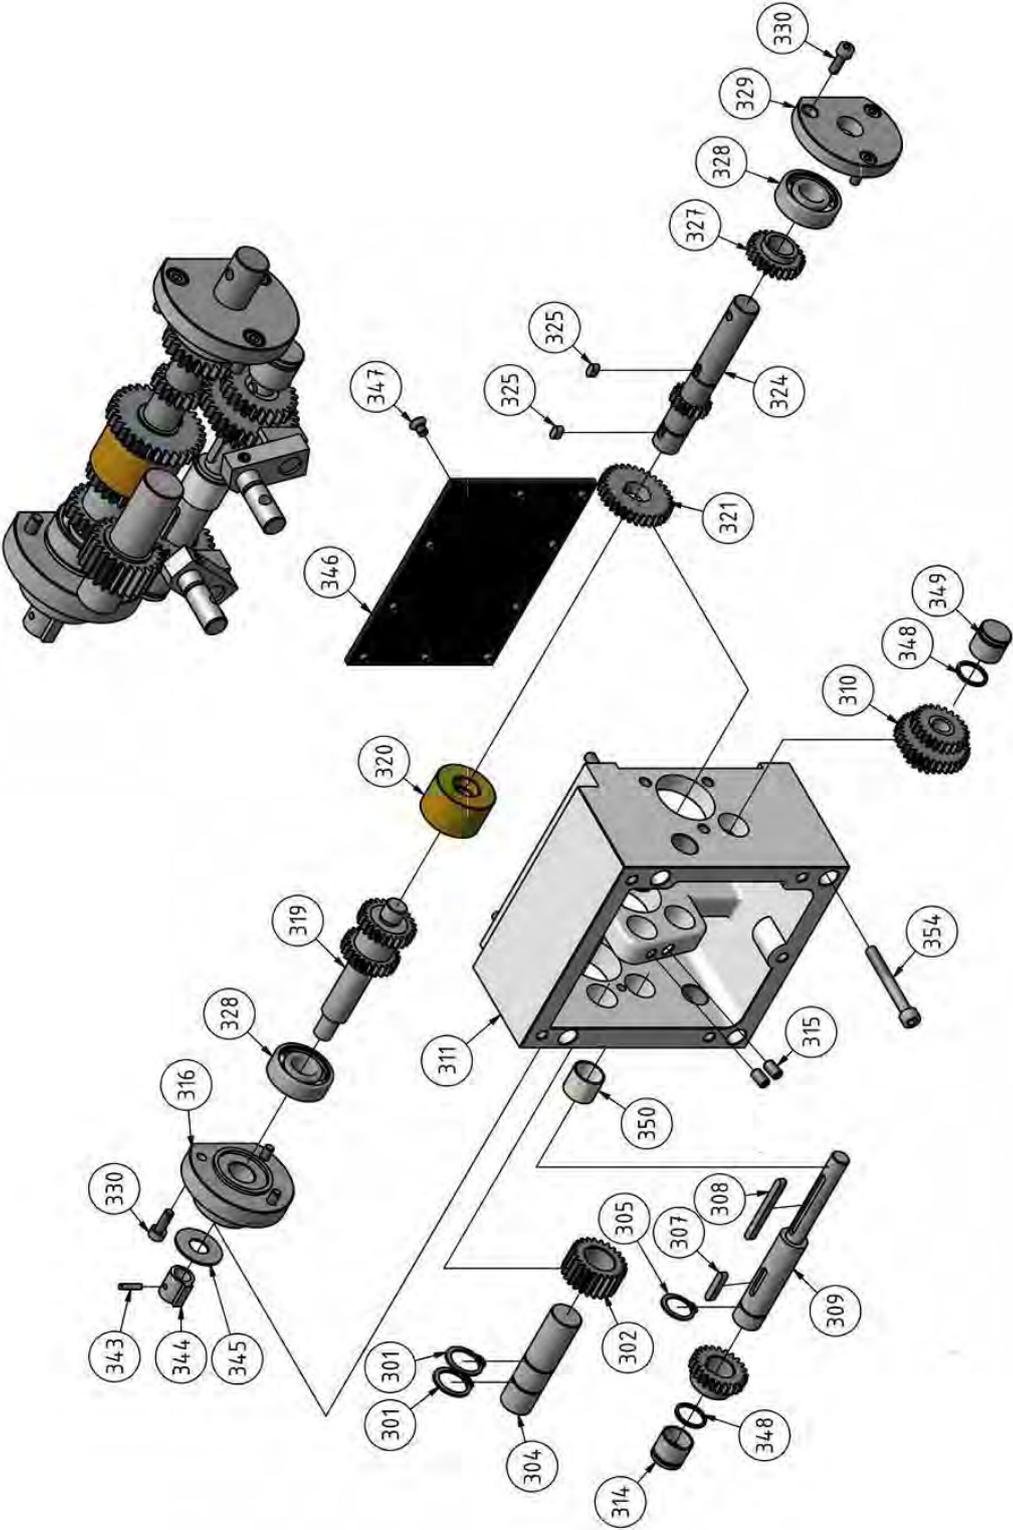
Vorschubgetriebe 2 von 2 - Engranaje de avance 2 de 2 - TU2506
